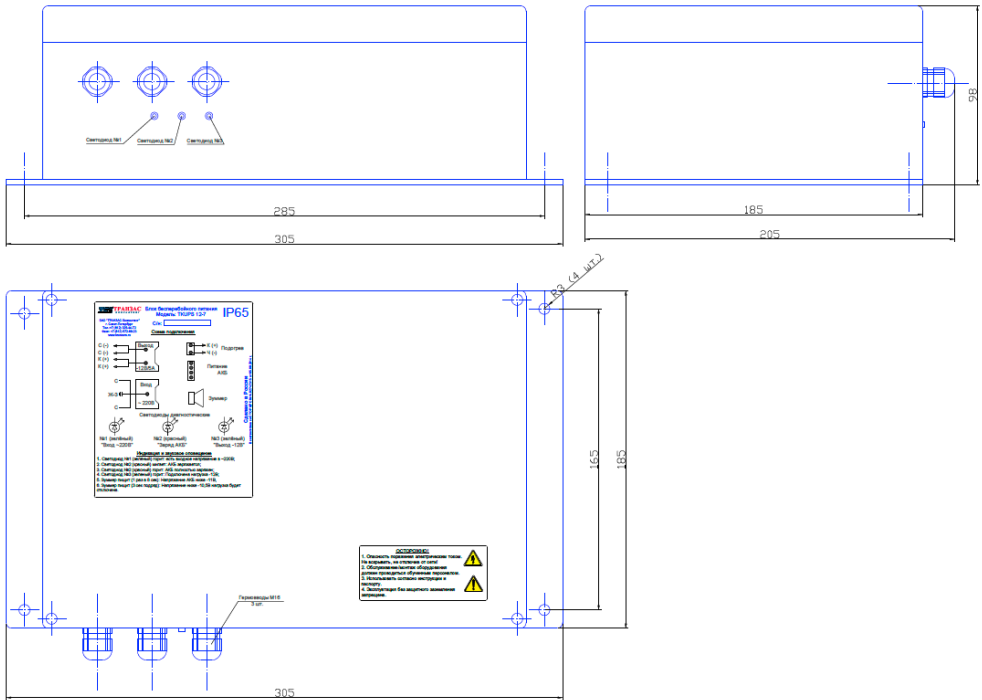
Габаритный чертёж ТКUPS-12-7/24-7
